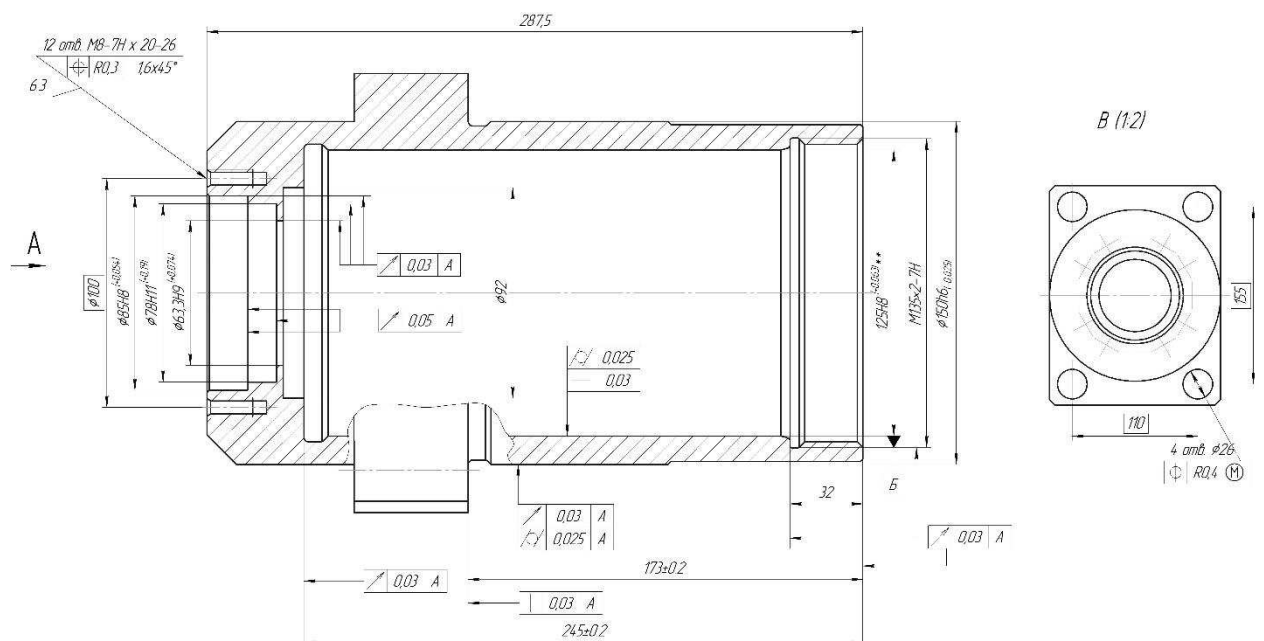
Допуска детали «Цилиндр»
